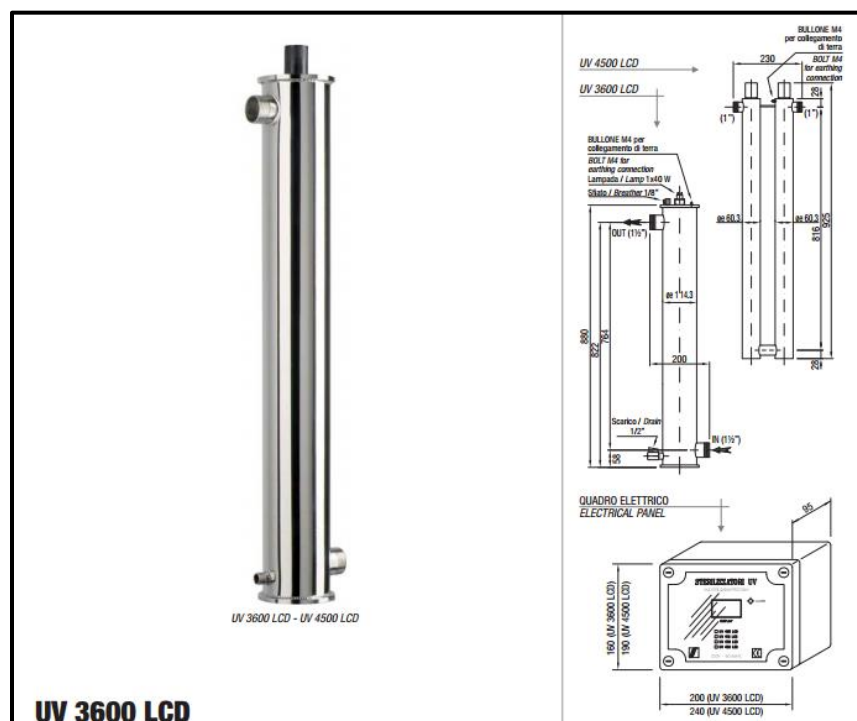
Imagen de filtro (de izquierda) y medidas (derecha). Anexo C
